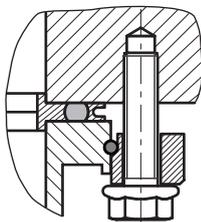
Flanschverbindung ISO-K zu ISO-F, Sechskantschraube und Gewindebohrung
